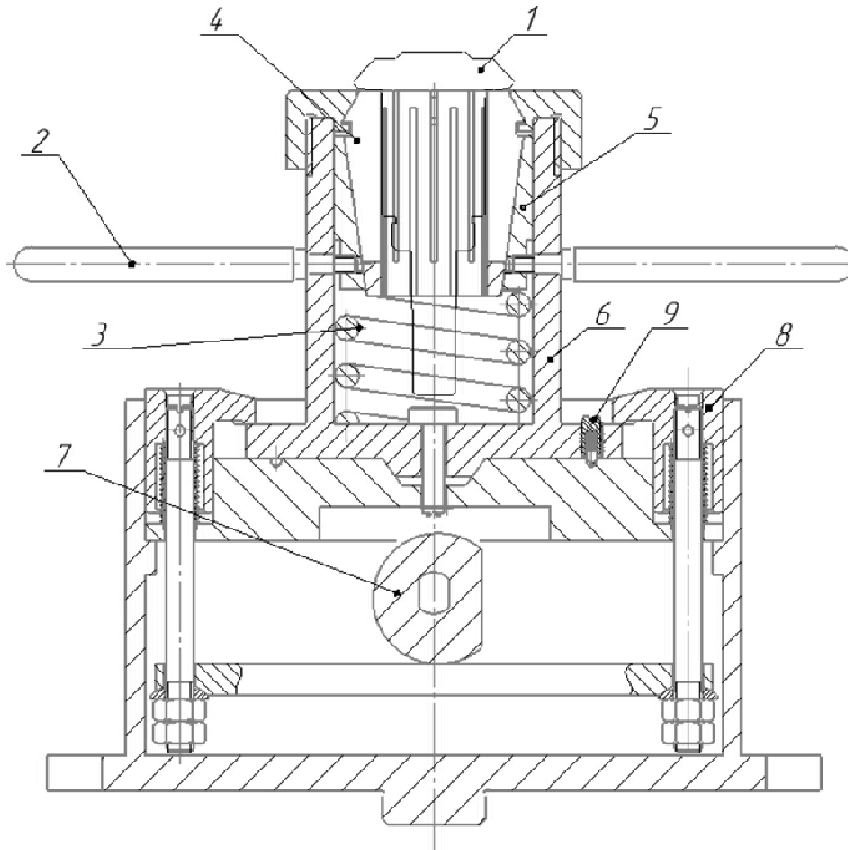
Схема пристосування. 1 – заготовка, 2 – важіль, 3 – пружина, 4 – цанговий патрон, 5 – втулка, 6 – корпус, 7 – кулачок, 8 – прихвати, що фіксують, 9 – гвинт-фіксатор
